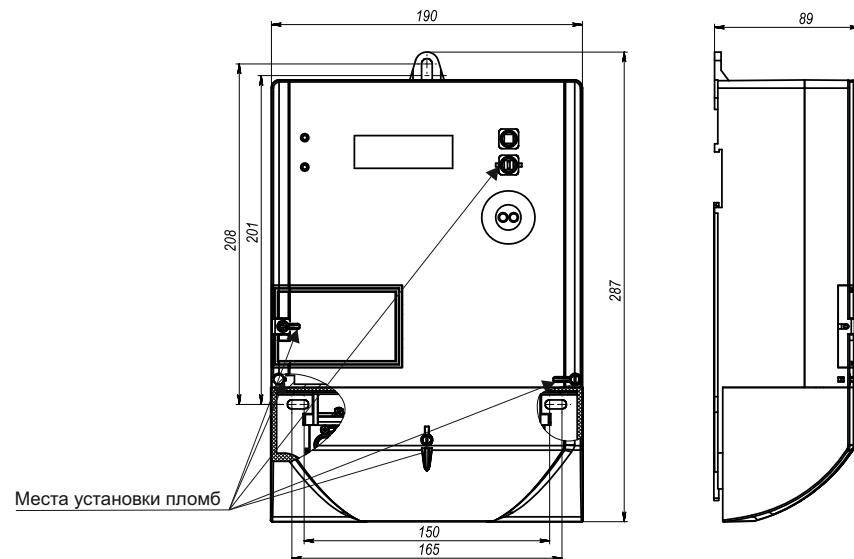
Общий вид, габаритные и установочные размеры, места установки пломб трехфазного счетчика трансформаторного включения типа МТХ 3
